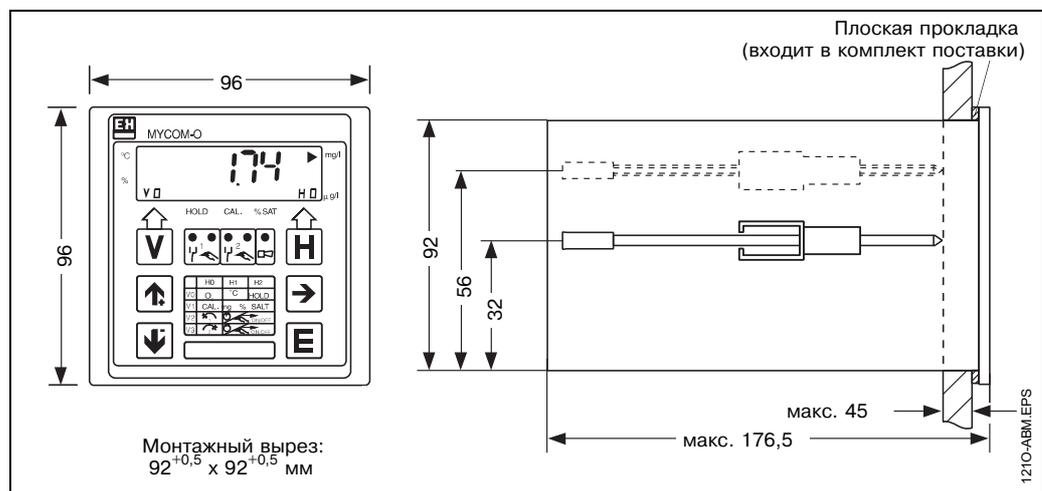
Габаритные размеры MYCOM COM 121 / 151
